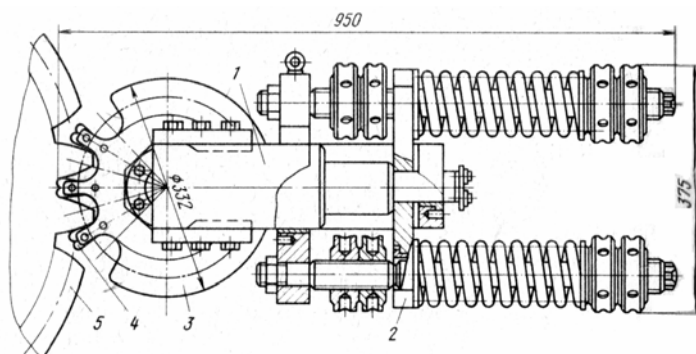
Устройство для поперечного обкатывания зубчатого колеса бортовой передачи экскаватора на токарном станке
